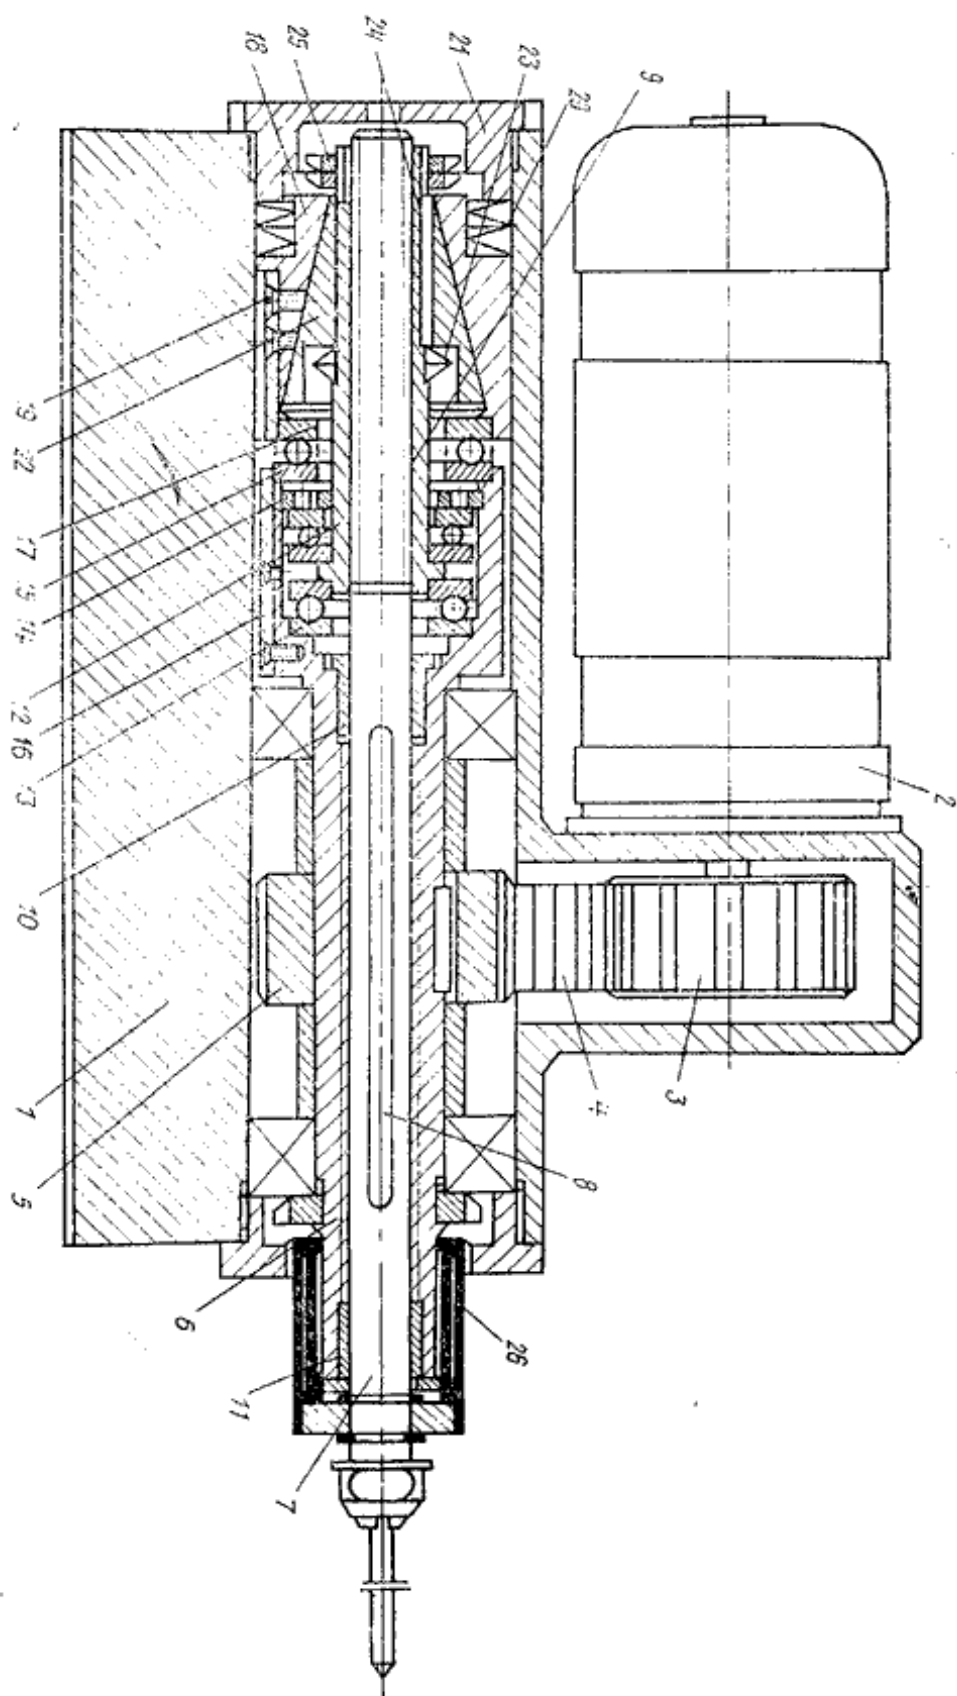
Пристрій для дискретної подачі шпинделя свердильного верстата.[18]
